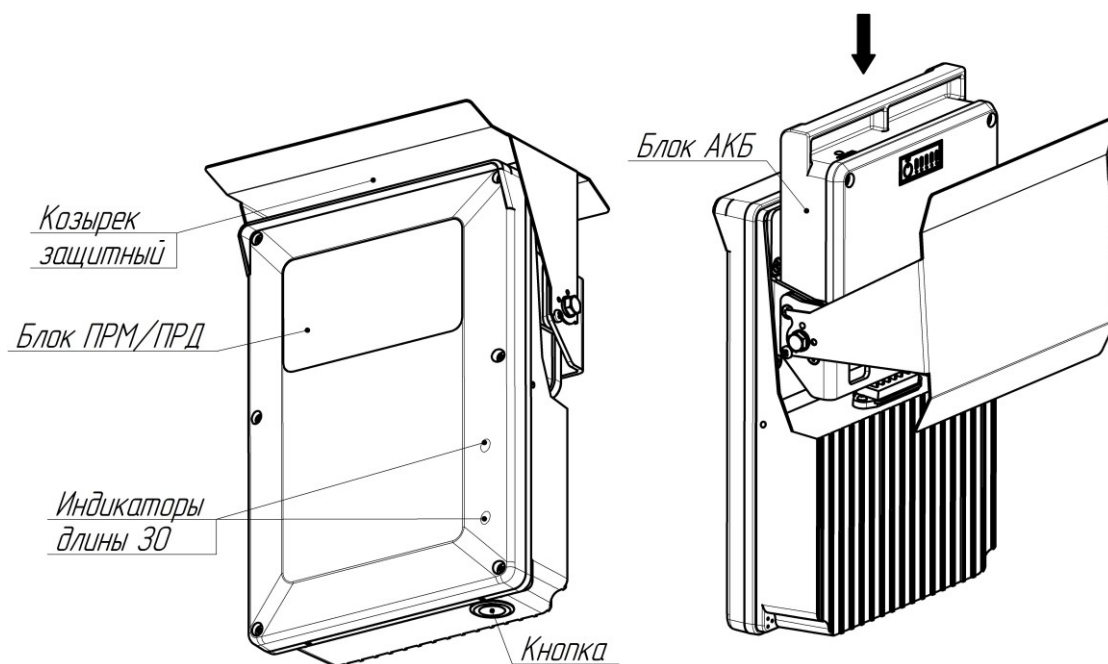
Внешний вид блока ПРМ-ПРД
